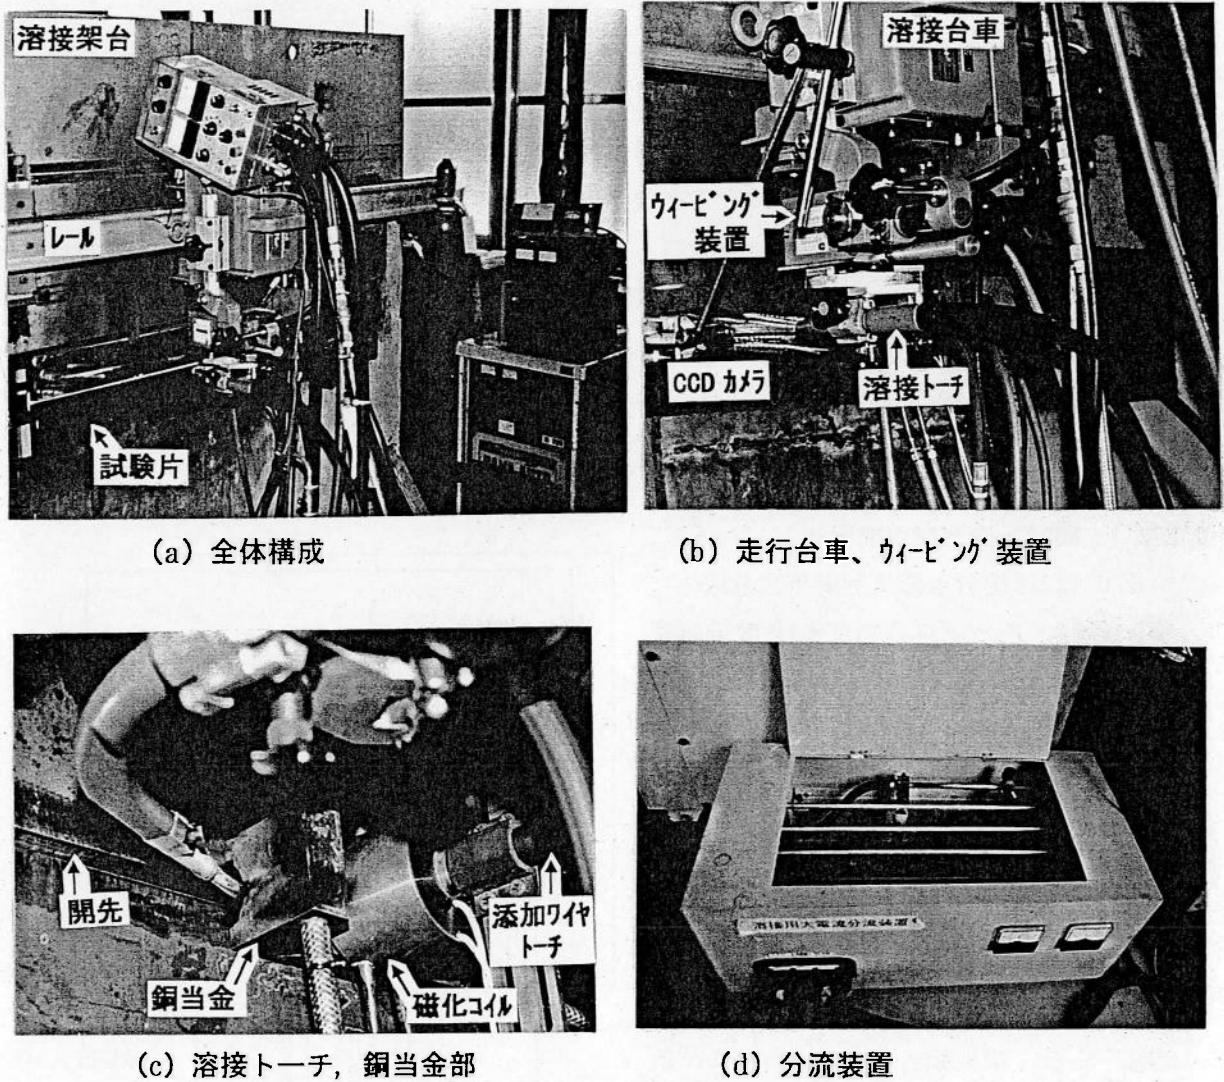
試作した横向姿勢エレクトロガスアーク溶接装置の外観
